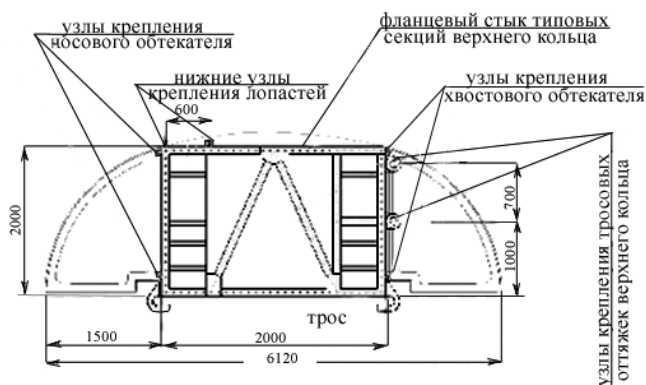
Фрагменты конструкции верхнего кольцевого ротора
